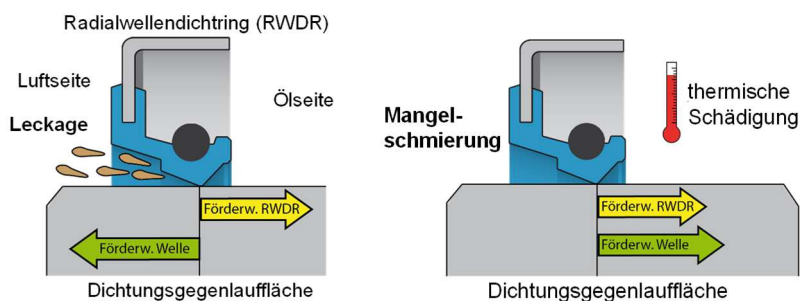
links: Leckage aufgrund entgegengesetzter Förderwirkung;
